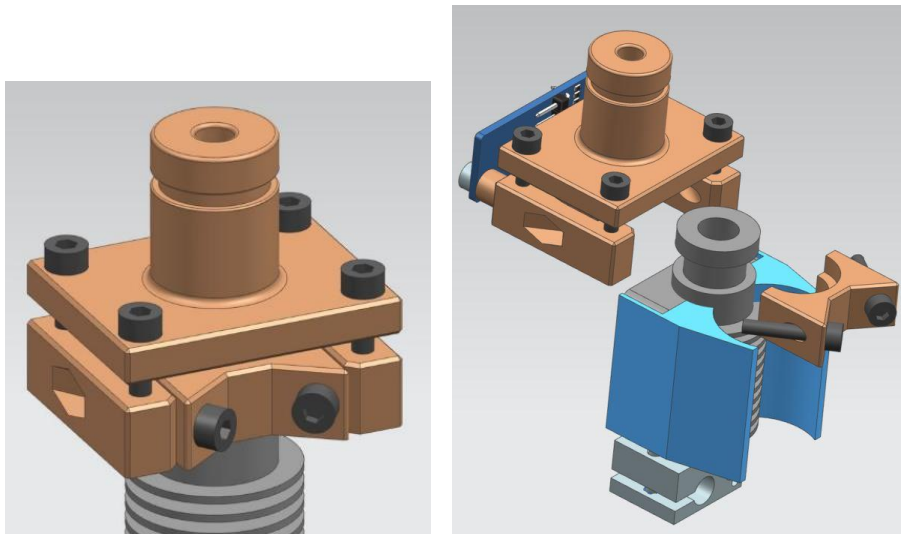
Variante A des Piezogehauses und Explosionsansicht der Hot Endbefestigung
